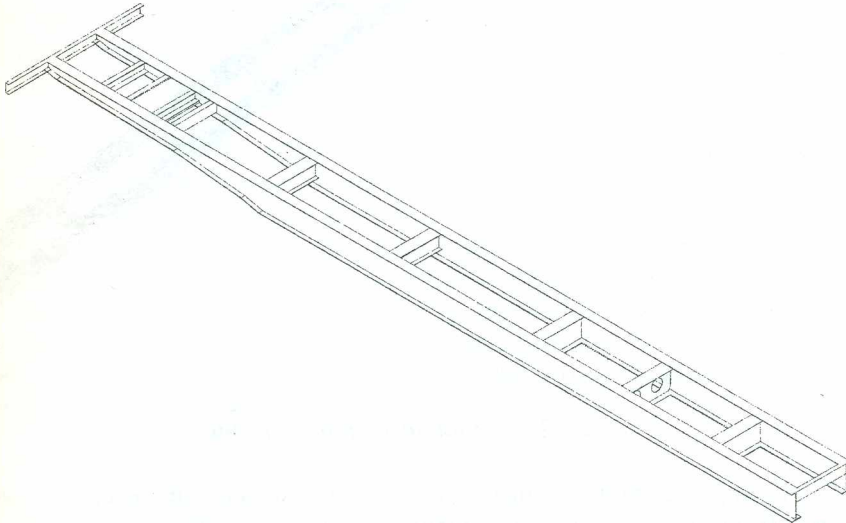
Конструкція основної несучої частини рами напівпричепа
